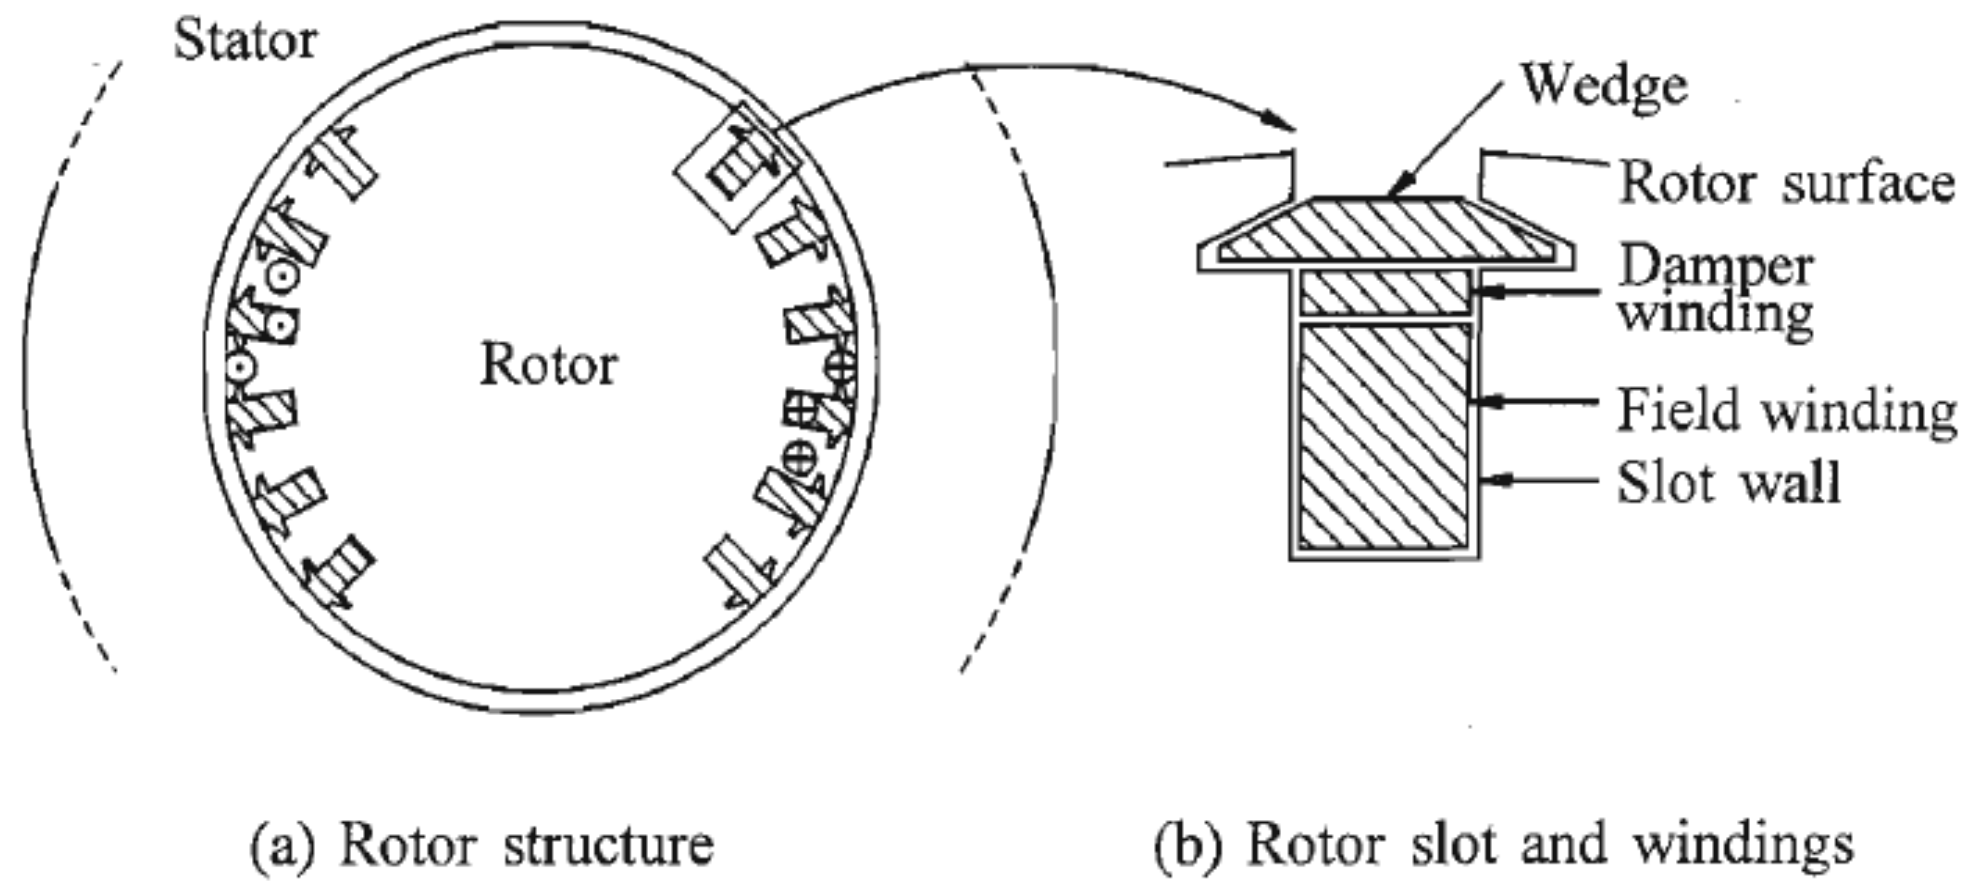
Corte Transversal de una Máquina Síncrona de Rotor Cilíndrico
